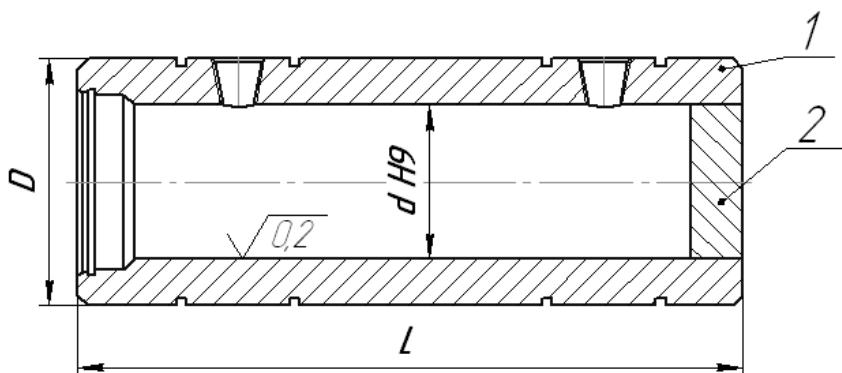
Сборно-сварная конструкция корпуса гидроцилиндра:
